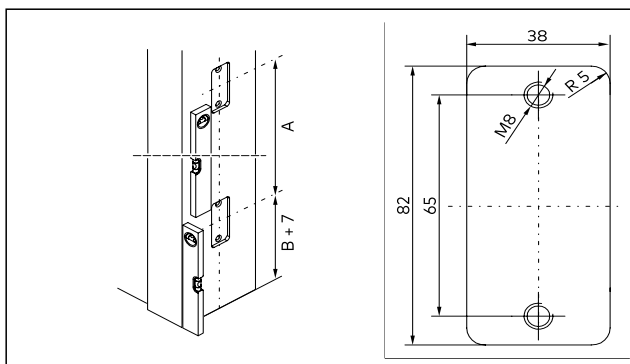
Schéma de dimensions pour les évidements des plaques de montage dans le châssis
